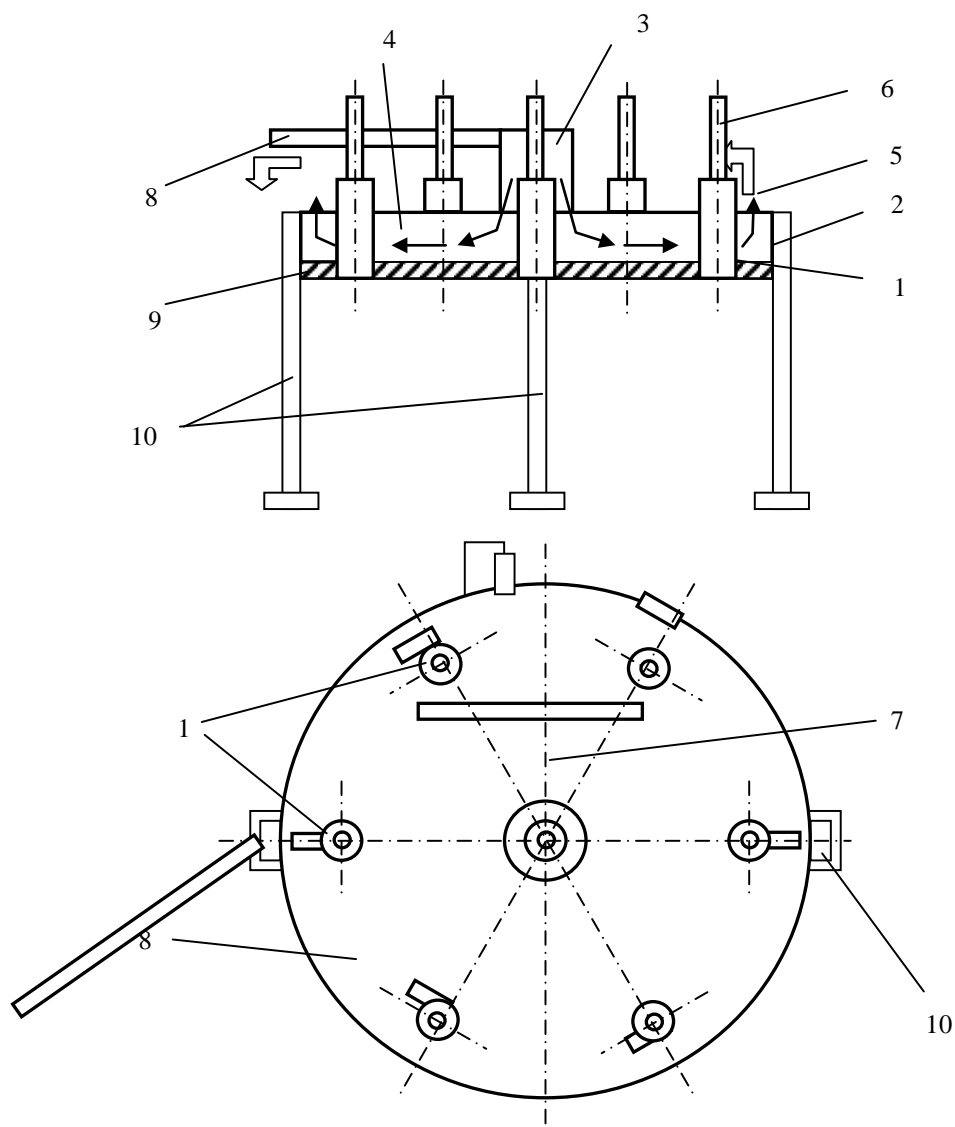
Главный вид и вид сверху теплового агрегата
